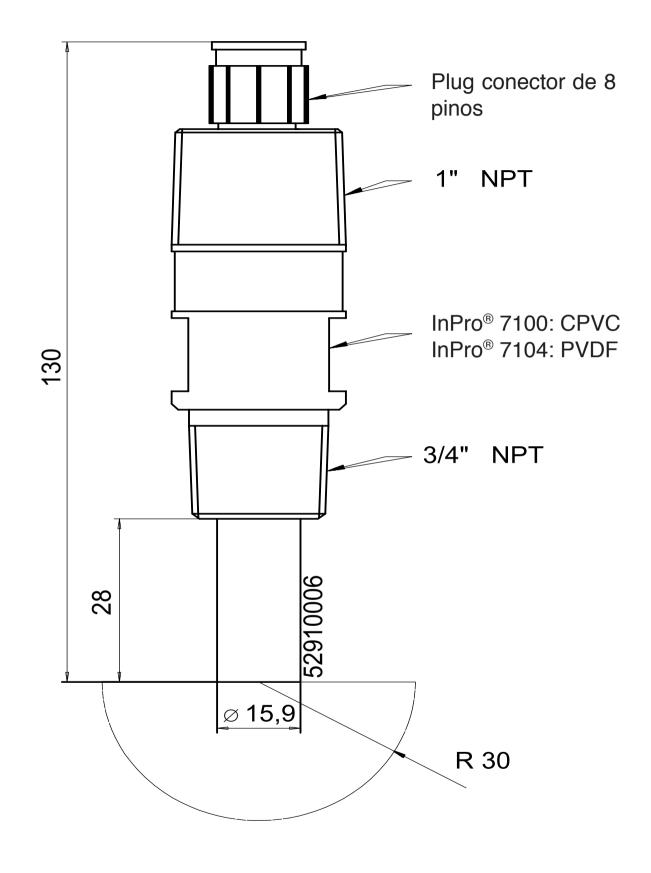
Desenho das dimensões do InPro® 7100/7104 com célula com 4 eletrodos
